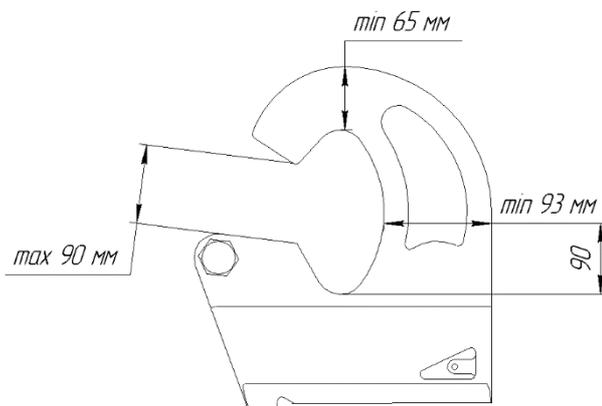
Допускаемые размеры крюка оборудования
